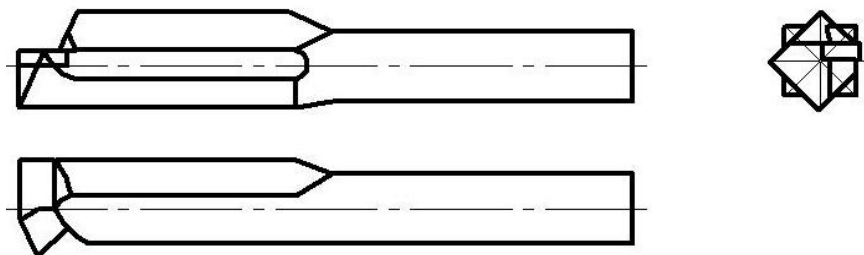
Скрученный расточный резец конструкции В. К. Семинского
